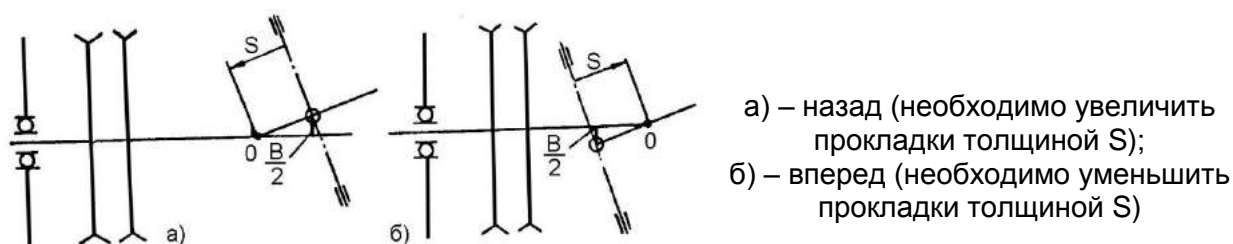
Схема регулирования пересечения осей кривошипного вала, крестовины и вилки вала шайбы при смещении эксцентриситета вращения
